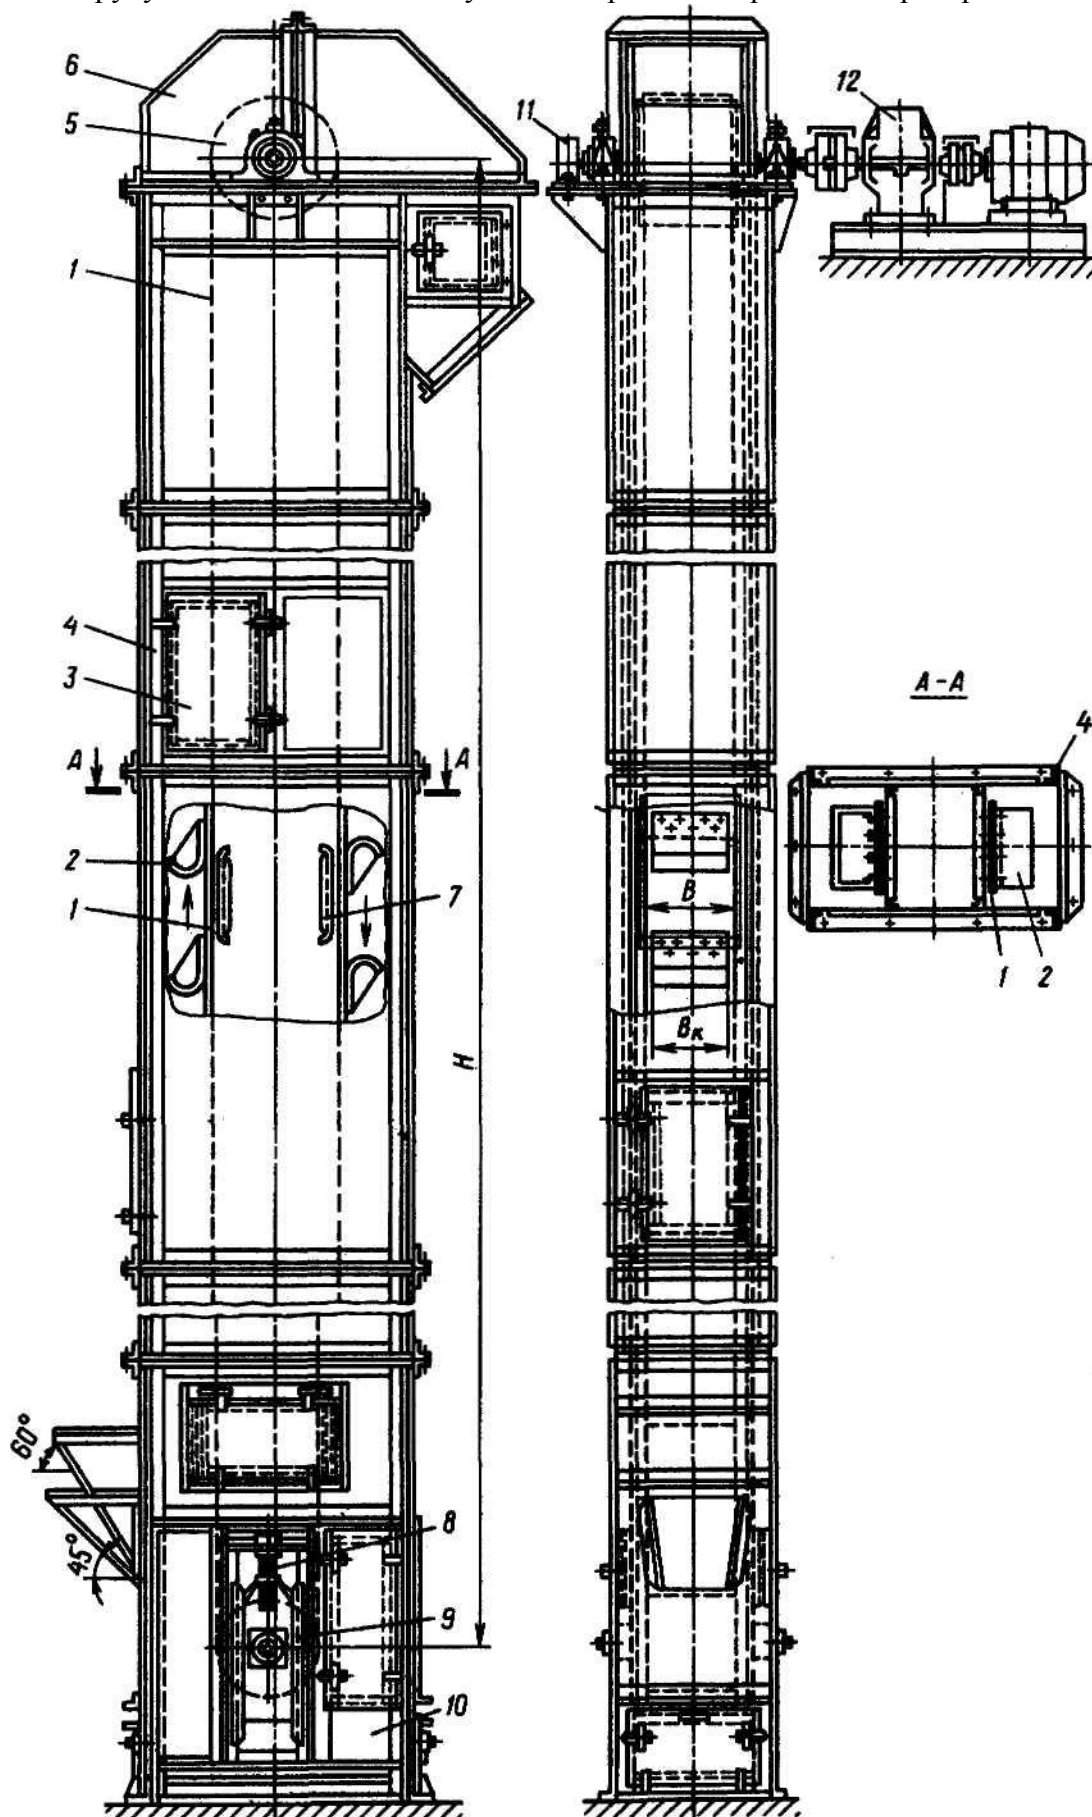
Вертикальний ковшовий стрічковий елеватор
